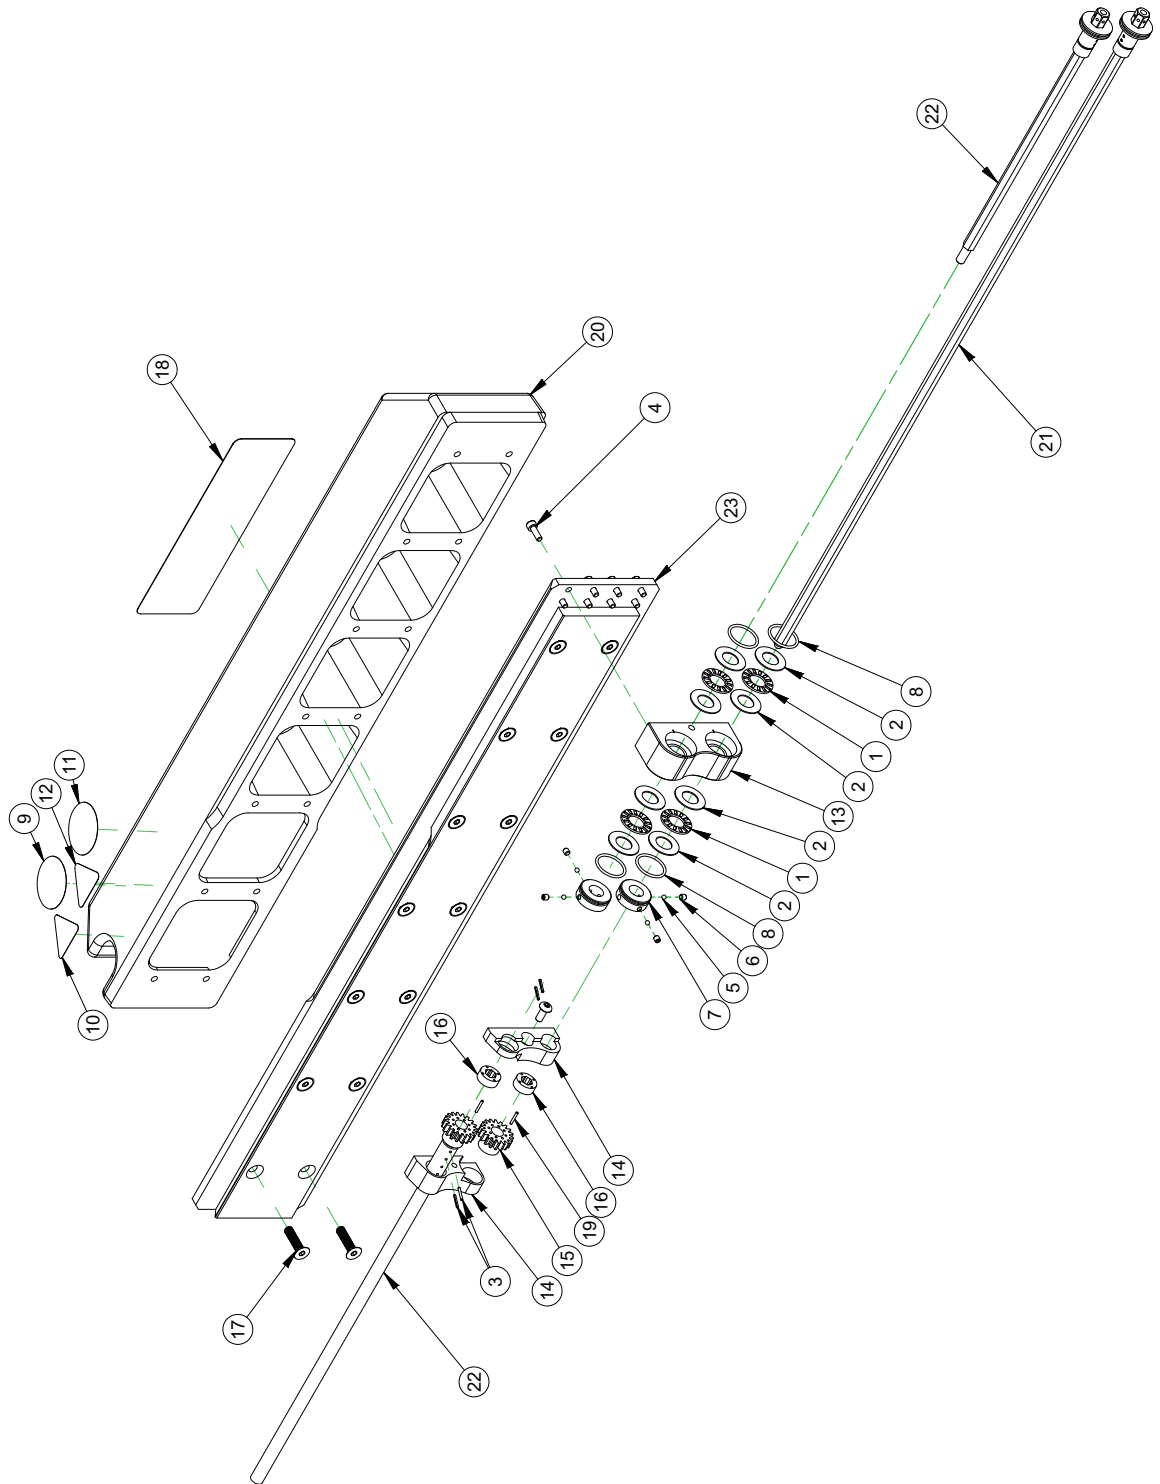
ENSEMBLE BRAS D'USINAGE (P/N 90337 RÉVISION D)
